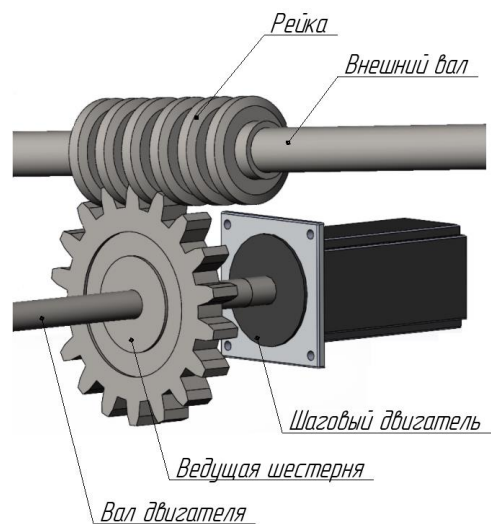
Общий вид реечного механизма для передачи возвратно-поступательного движения
